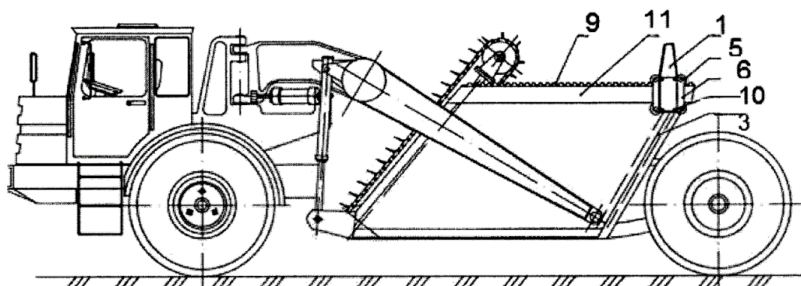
Общий вид скрепера с элеваторной загрузкой и предлагаемым механизмом выдвижения задней стенки: 1 – рама; 2 – планетарный гидромотор-редуктор; 3 – задняя стенка; 4 – шестерни; 5 – колеса; 6 – ходовая тележка; 7 – боковые стенки ковша; 8 – ролики; 9 – зубчатая рейка; 10 – болты; 11 – боковые балки ковша
